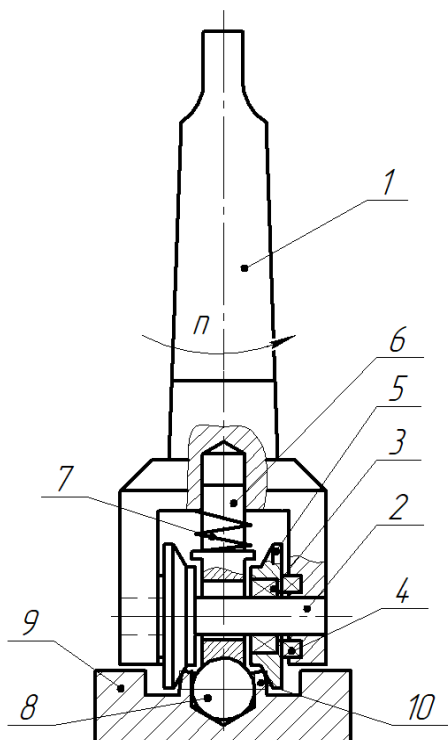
Конструкція інструмента для завальцьовування кульок у циліндричні втулки
